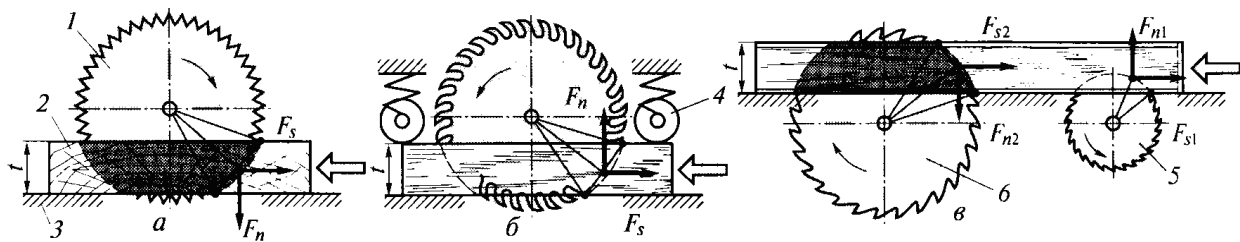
Схема пиляння з верхнім (а, б) і нижнім (в) розташуванням пилки: 1 – пилка; 2 – заготівка; 3 – базувальний елемент верстата; 4 - притискний елемент; 5 - підрізна пилка; 6 - основна пилка; F_n - вертикальна складова сила різання; F_s - горизонтальна складова сила різання
